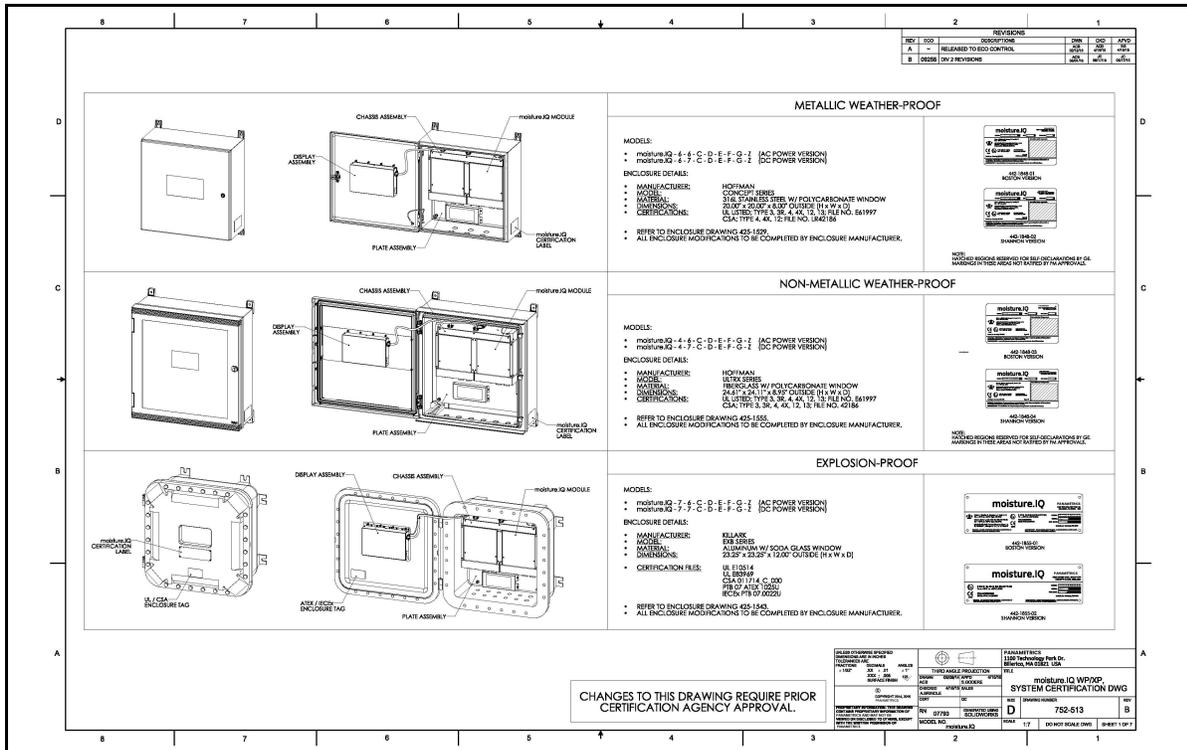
Systemzertifizierungszeichnung für wetter-/explosiongeschützte Version (Zeichnung 752-513_revB, Blatt 1 von 5)
